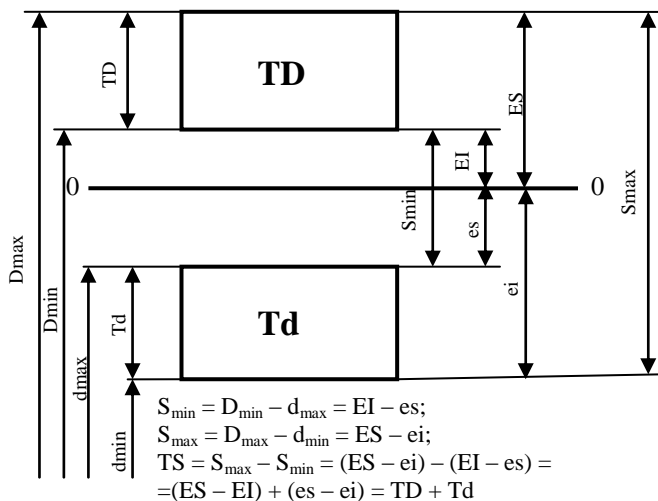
Схема расположения полей допусков при посадке с зазором
